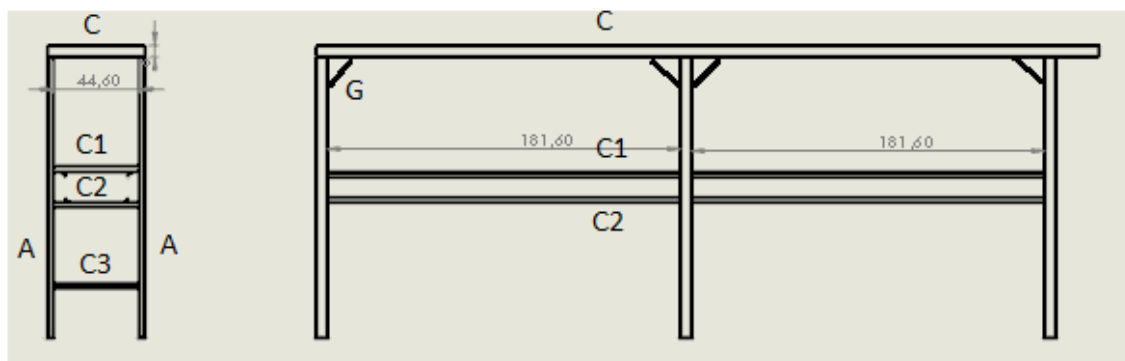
Esquema general de la estructura aporticada tipo puente grúa
